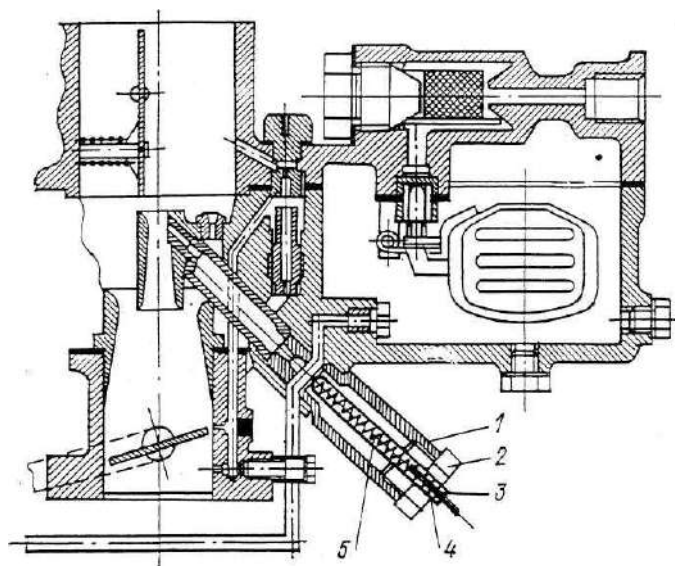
Испаритель топлива в карбюраторе: 1 – корпус электронагревателя; 2 – пробка; 3 – ТЭН; 4 – контактный стержень; 5 – спираль.
